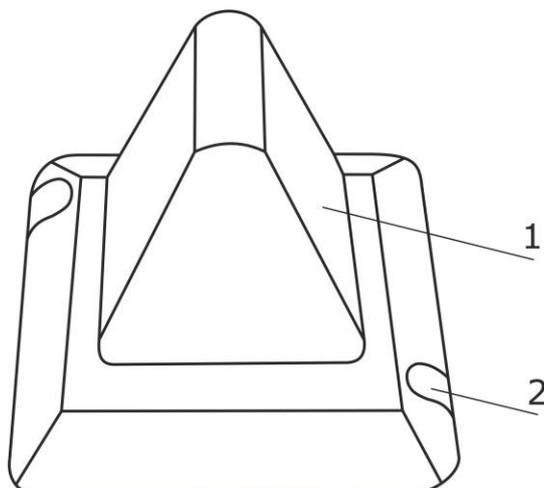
Внешний вид радиоконтроллера MP-211W1
